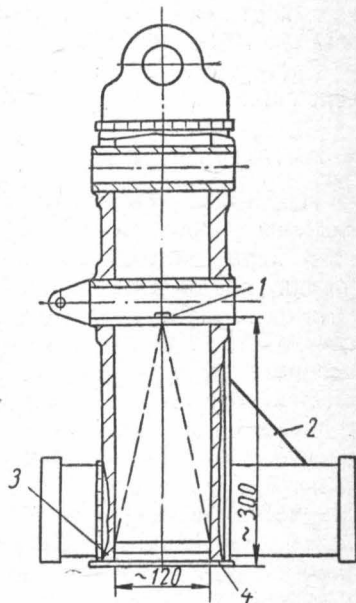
Схема установки для просвечивания сложного сварного узла:
